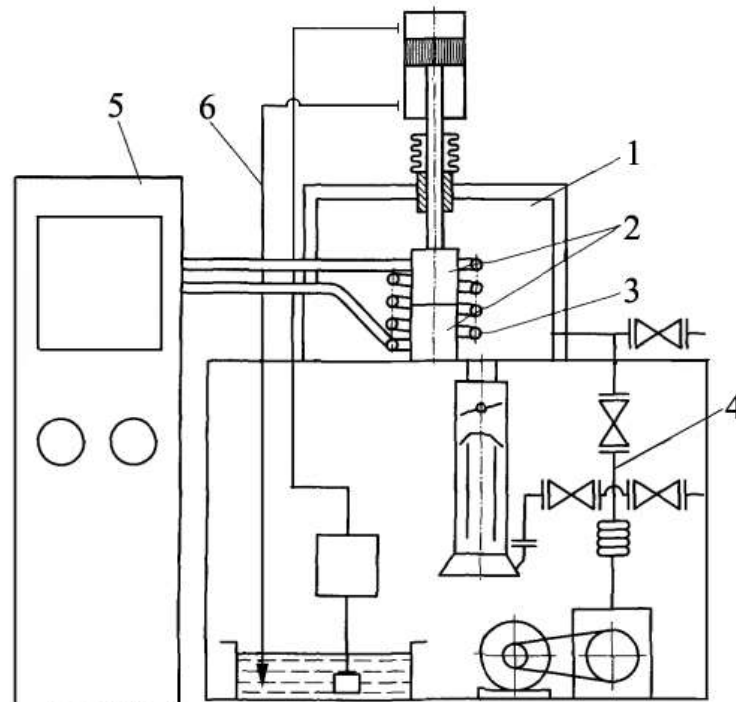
Схема дифузійного зварювання у вакуумі
